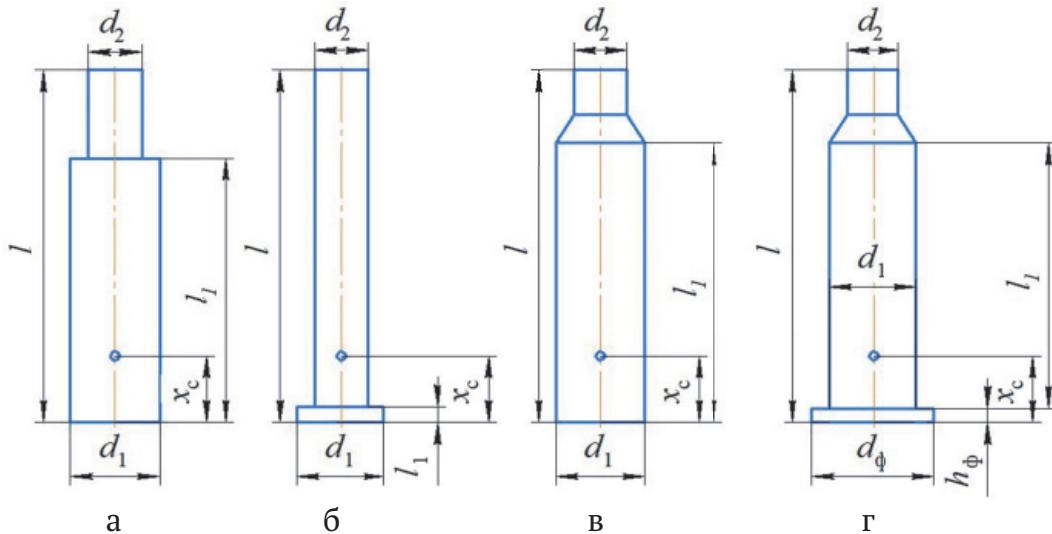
Стержневые цилиндрические (а, б) и сложной формы (в, г) ступенчатые заготовки и их основные геометрические параметры
